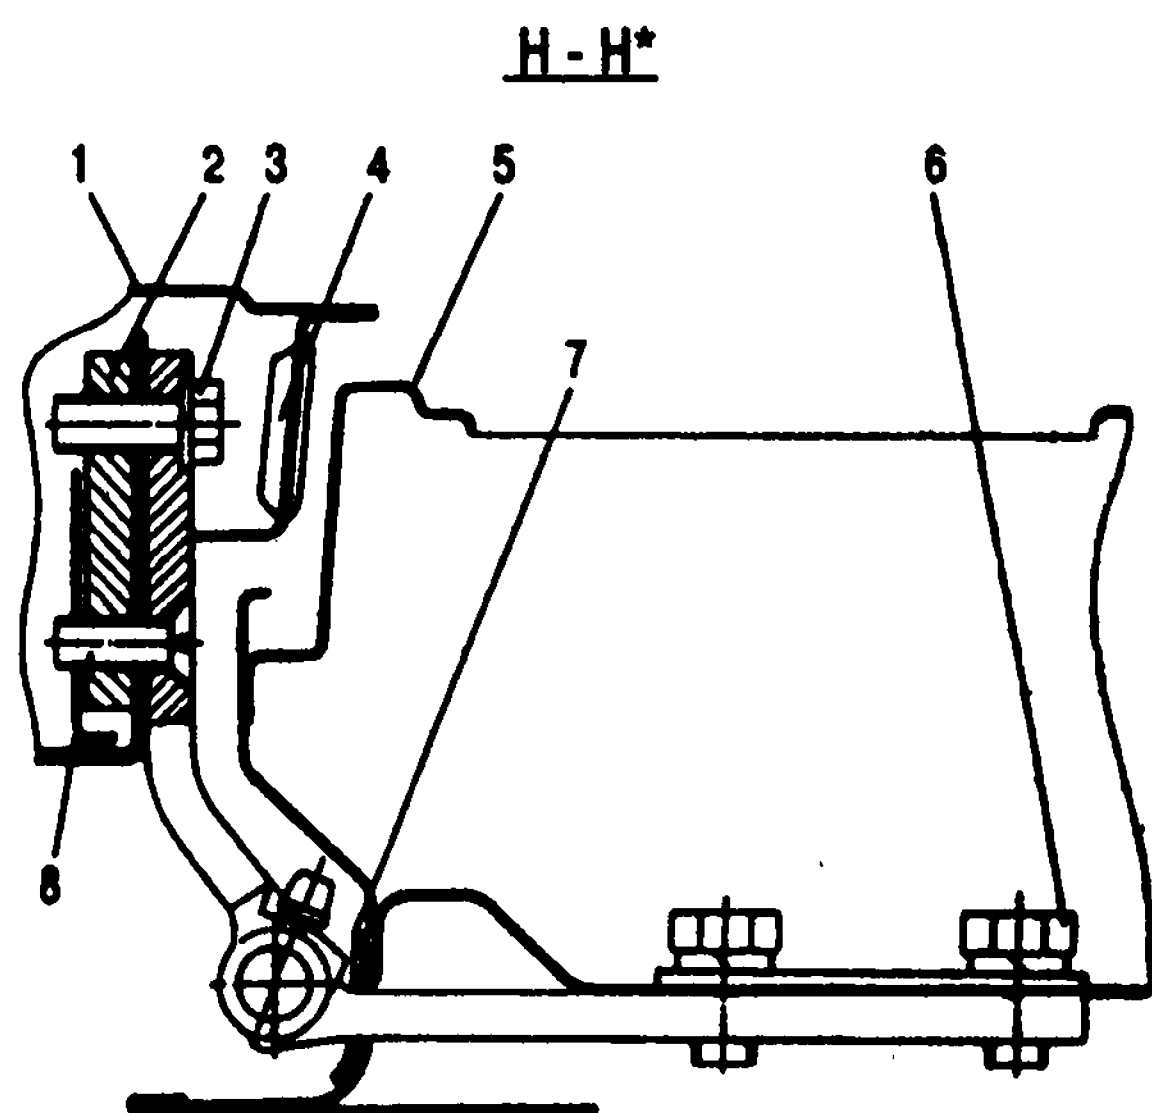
Петля задней двери: 1 - центральная стойка; 2 - пластина; 3 - болт М10 крепления петли к стойке; 4 - заглушка; 5 - дверь задняя; 6 - болт М8 крепления петли к двери; 7 - уплотнитель петли на двери; 8 - винт М8 крепления петли к стойке (верхняя петля)
